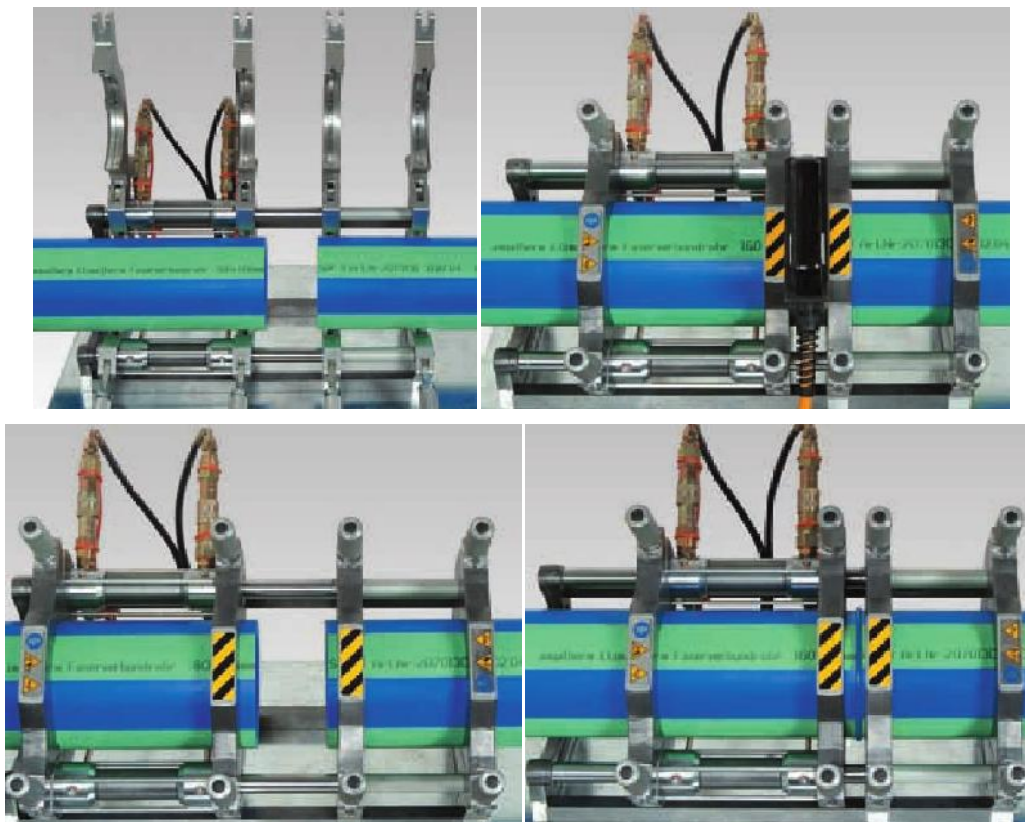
Procedimento de soldadura topo a topo em tubos de polipropileno [51]
